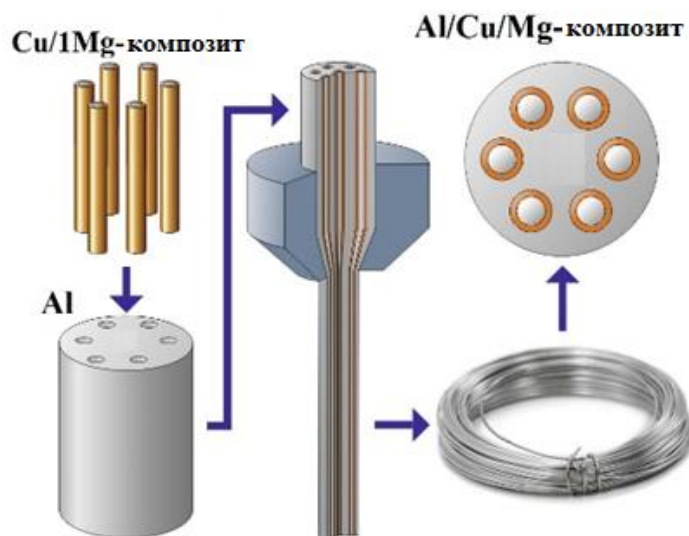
Схема изготовления тройного композита Al/Cu/Mg
